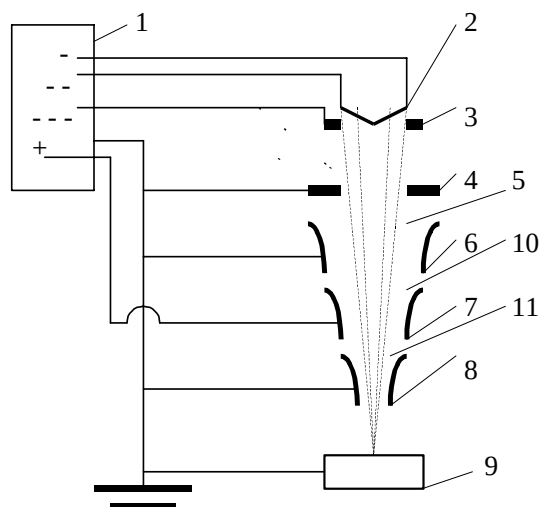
Общий вид устройства для электронно-лучевой сварки.
